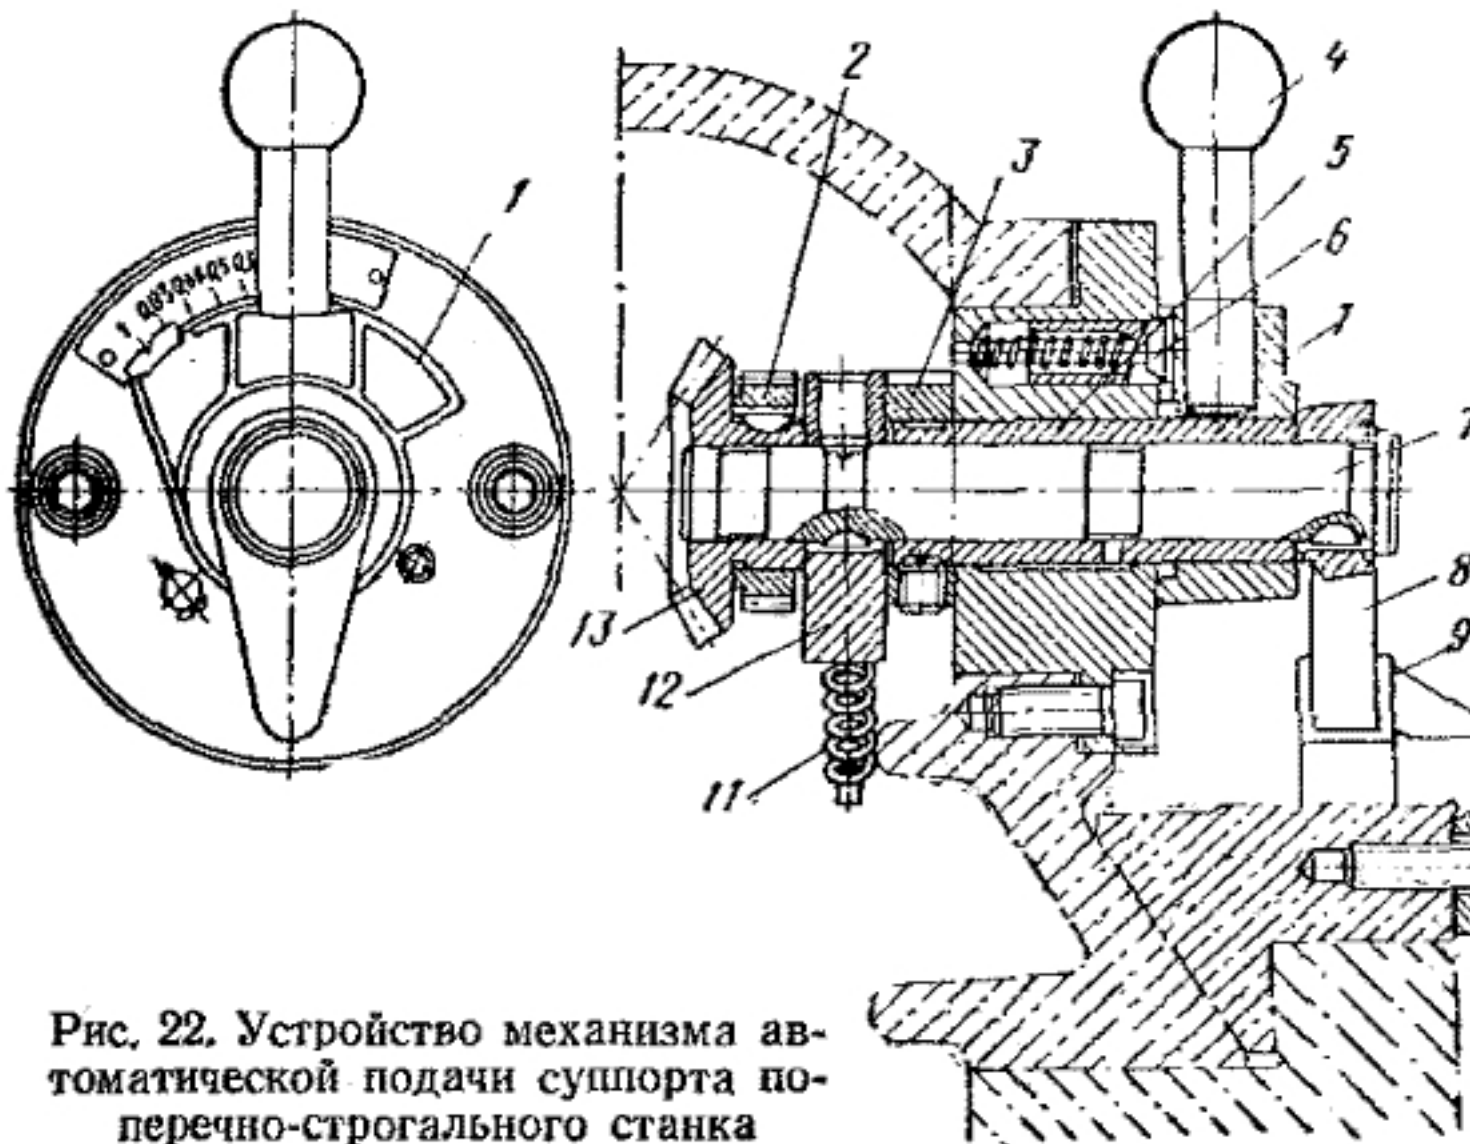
Устройство механизма автоматической подачи суппорта поперечно-строгального станка
